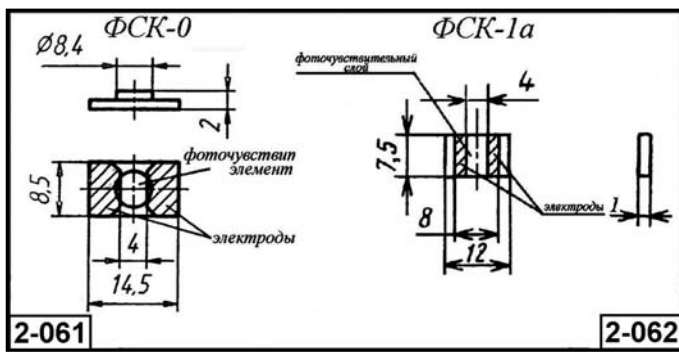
Внешний вид, габаритные размеры и ОСХ фоторезисторов на основе CdS
